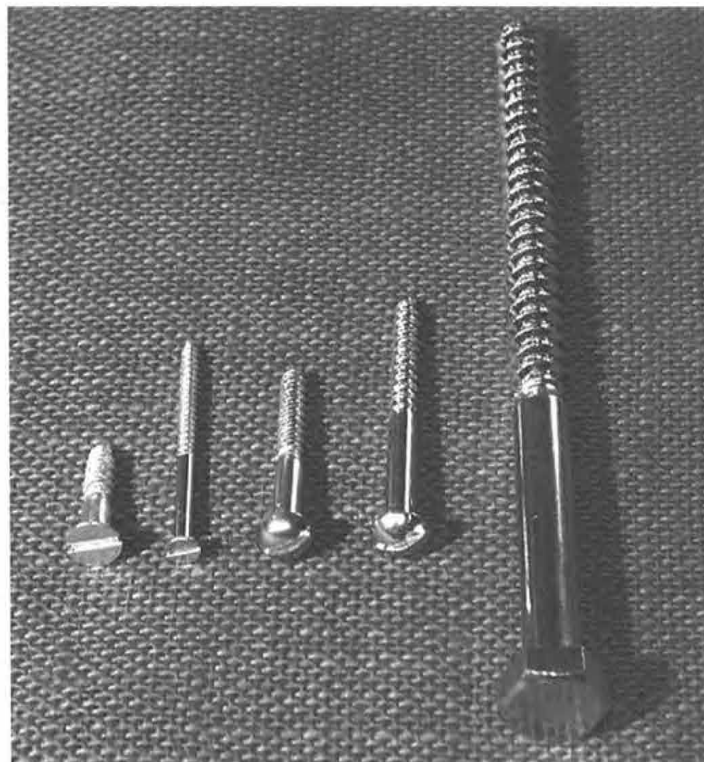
Holzschrauben mit Gewinde nach DIN 7998
